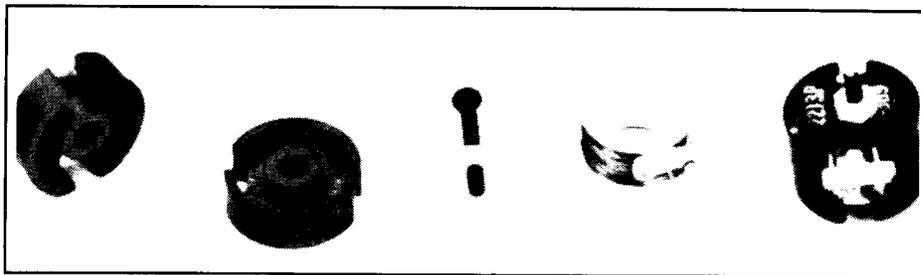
Assemblage à noyau magnétique dit pot core; le boîtier et la bobine à gauche; le tout assemblé à droite.
